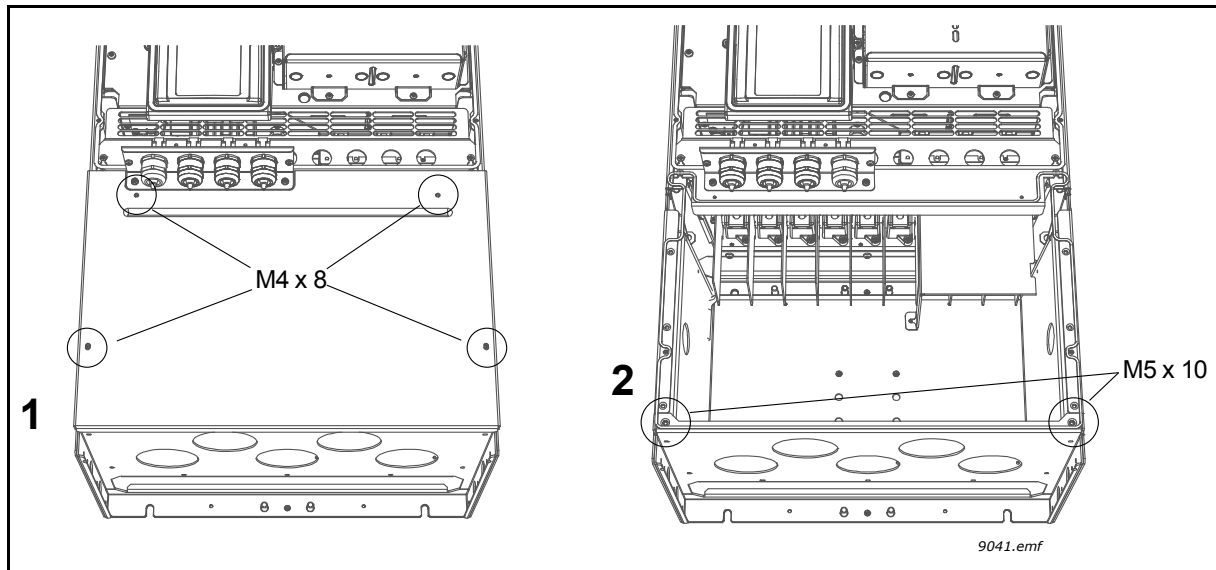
Removendo a tampa do cabo e a placa de fixação do cabo (MR9).
